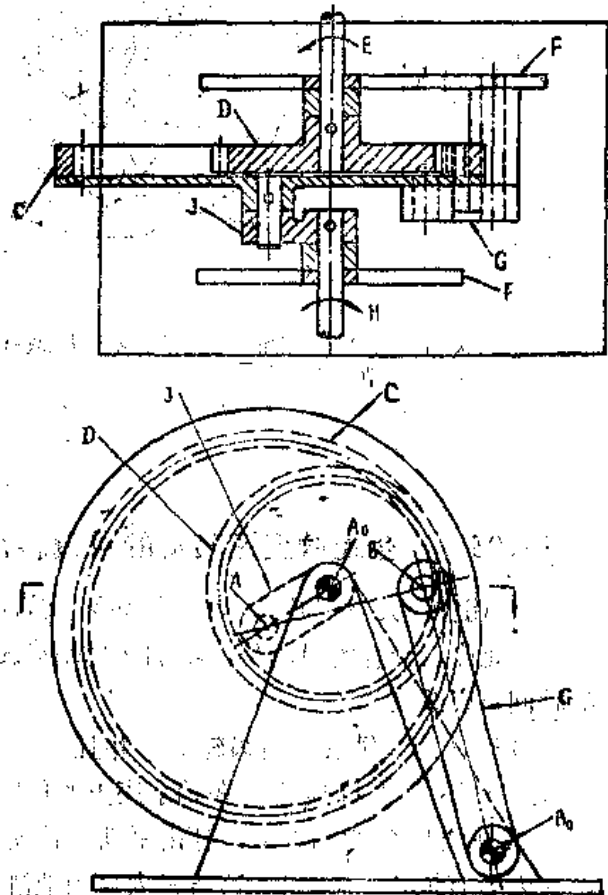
曲柄转移内齿轮，使与内齿轮啮合的外齿轮转动
